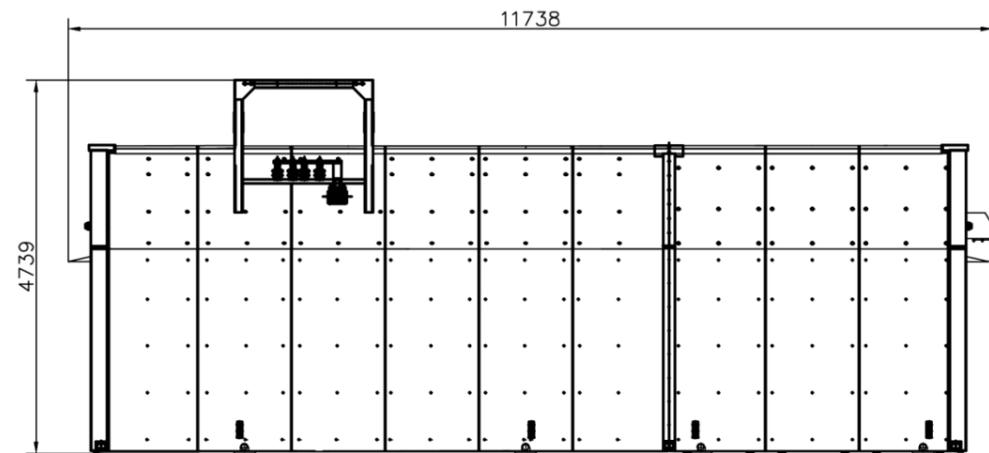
Габаритный чертёж ППВ-3М-4, с количеством фидеров - 4 шт., масса 13000 кг
